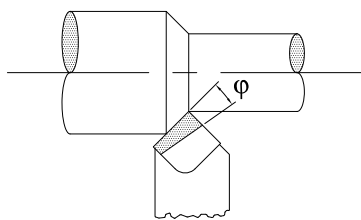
Kladný vrcholový úhel pro hlazení
